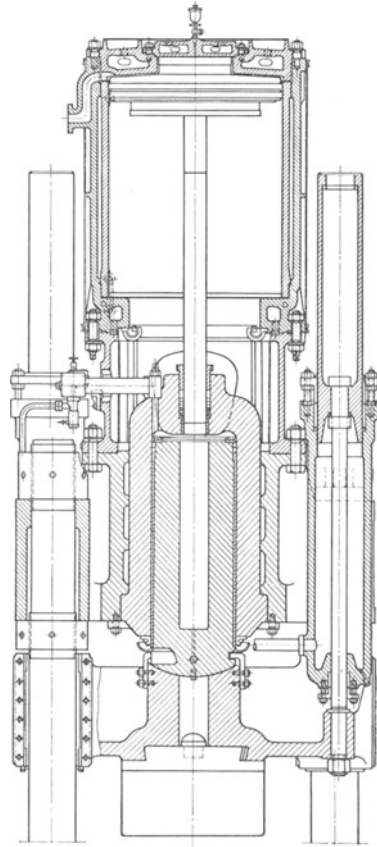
Preßzylinder einer 3000-t-Schmiedepresse mit aufgebautem Treibapparat.
